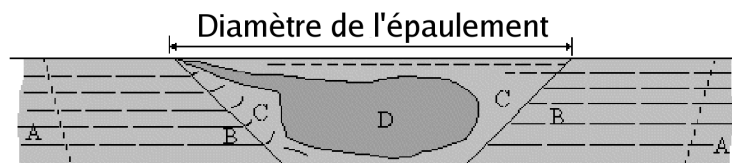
Illustration schématique d'un cordon de soudure par friction stir welding (la "zone retraits" se trouve à droite et la "zone d'attaque" à gauche).
